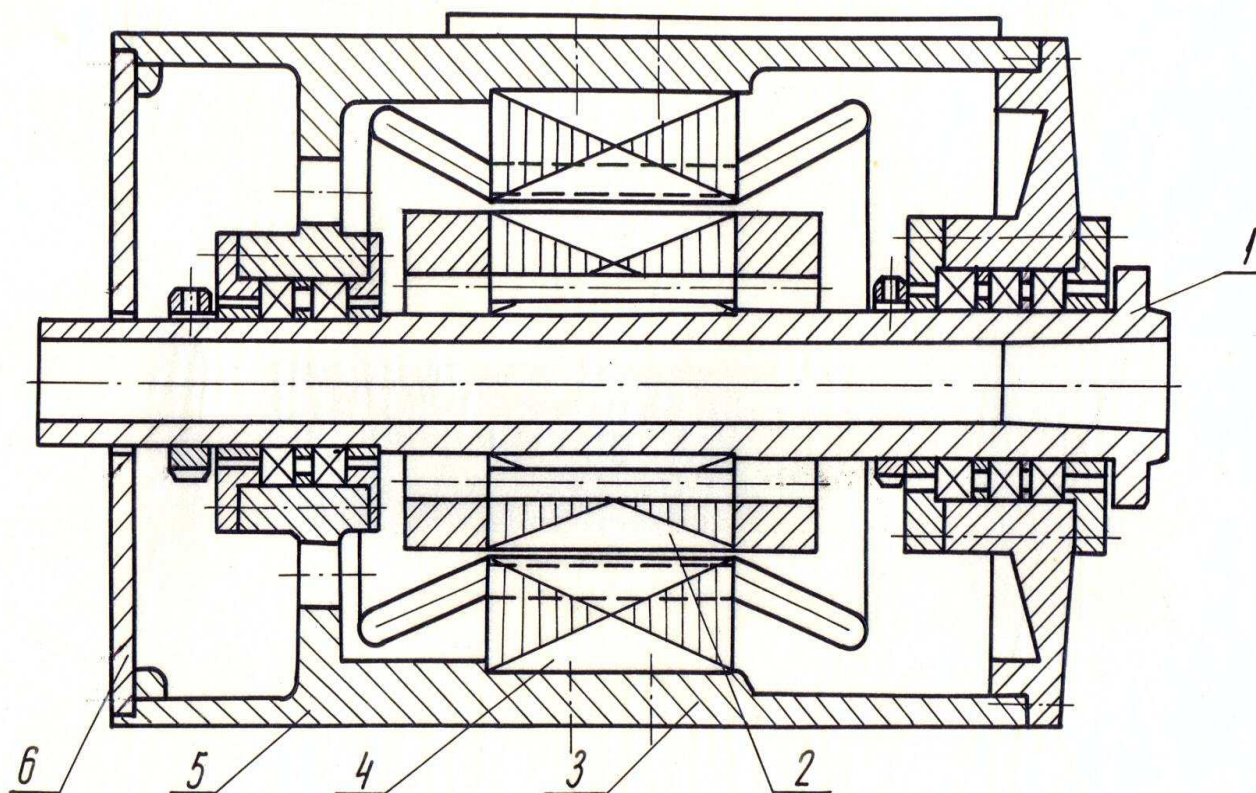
Схема МШ с аксиальной воздушной системой охлаждения: 1 – шпиндель; 2 – ротор; 3 – цилиндрический корпус статора; 4 – статор; 5 – корпус МШ; 6 – задняя стенка с вытяжными вентиляторами
